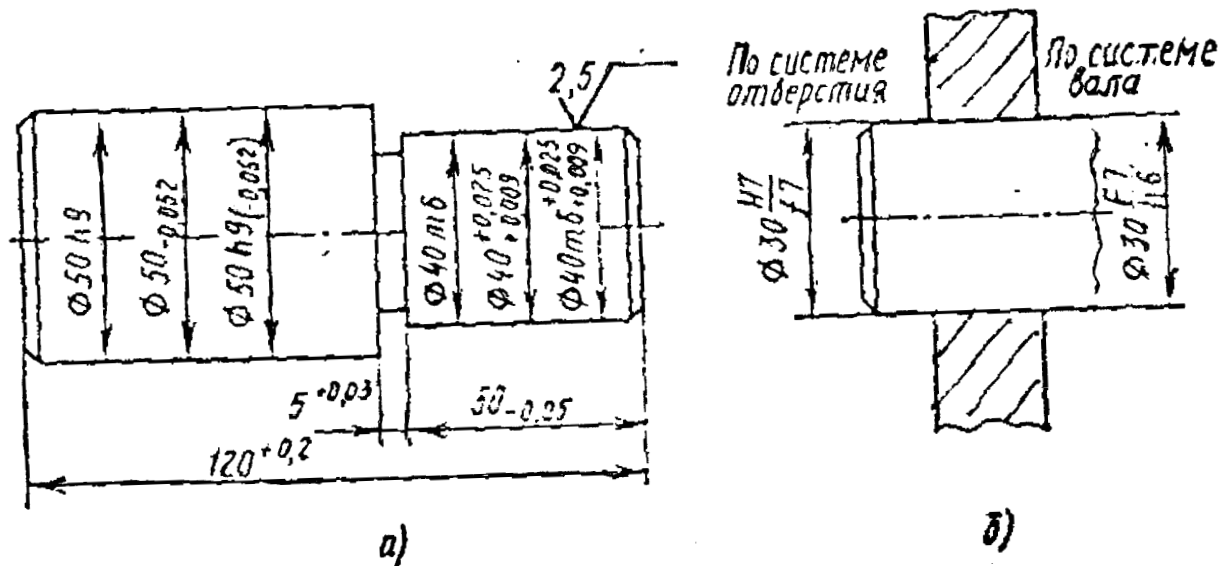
Пример обозначения допусков в рабочих чертежах:
